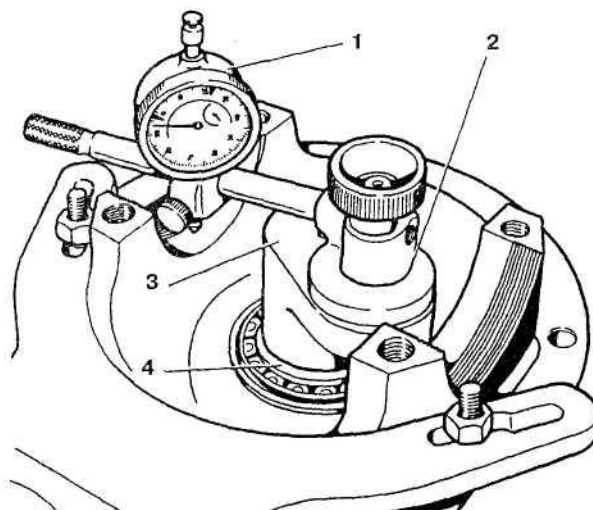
Определение толщины регулировочного кольца ведущей шестерни: 1 — индикатор; 2 — приспособление А.95690; 3 — задний подшипник ведущей шестерни; 4 — оправка А. 70184
